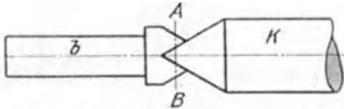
Kegelige Mikrometerspitzen zur Messung des Flankenmaßes.
